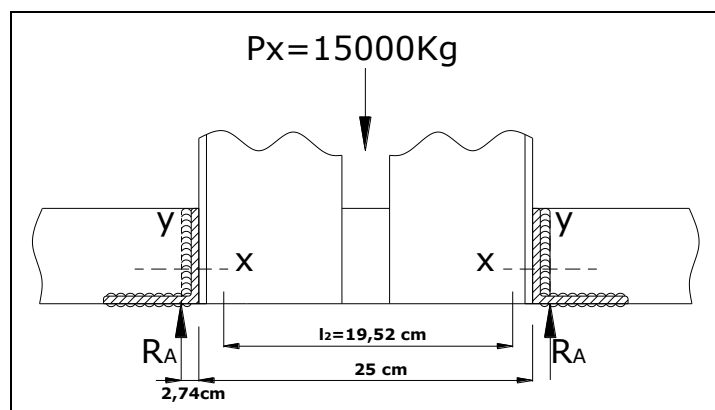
Momento flector de la soldadura de la base.
